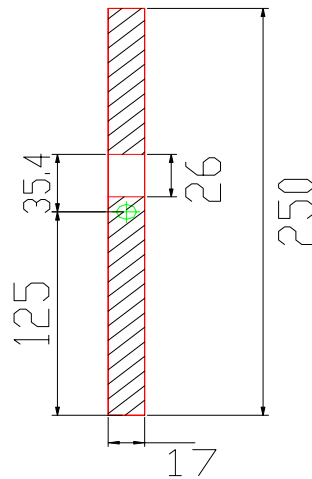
Dimensiones y posición del centroide de la sección transversal donde se produce la avería.
